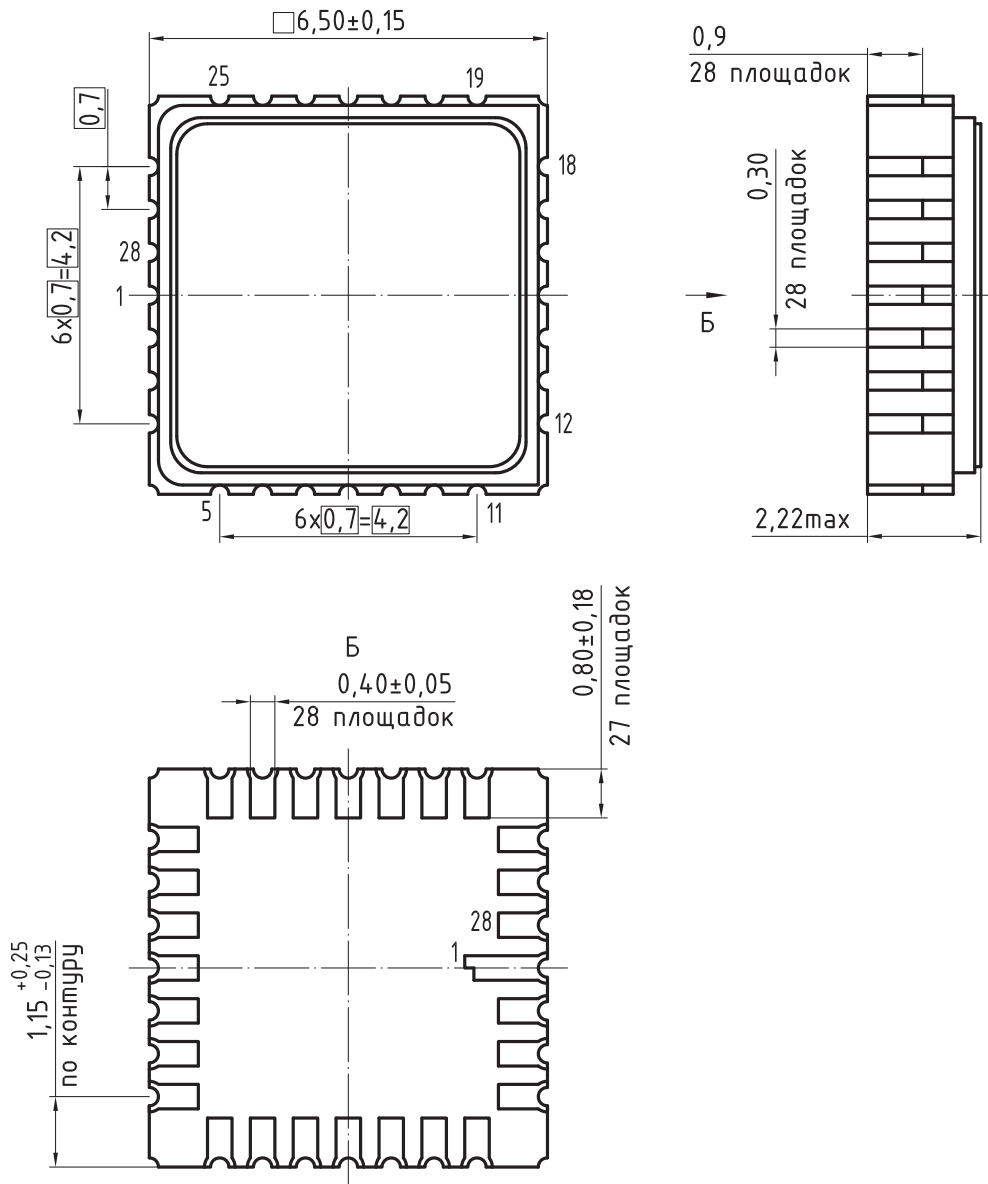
Чертёж корпуса 5123.28-1.01
